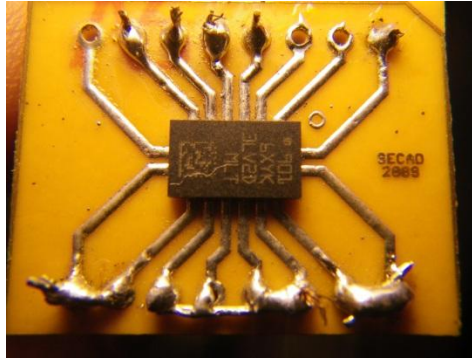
Acelerómetro LIS3LV02DL com encapsulamento LGA16 montado numa PCB
